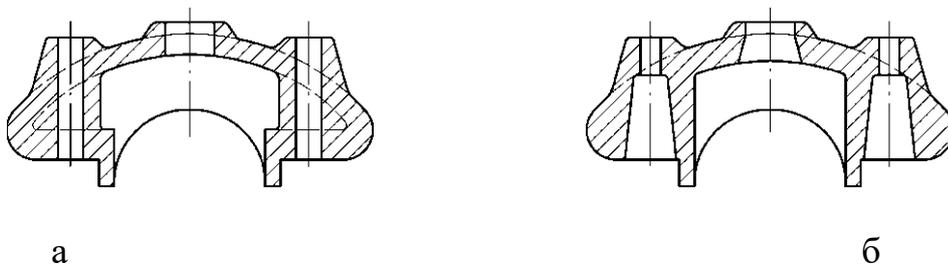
Крышка подшипника: а - формируется с применением стержня; б - формируется без стержня
